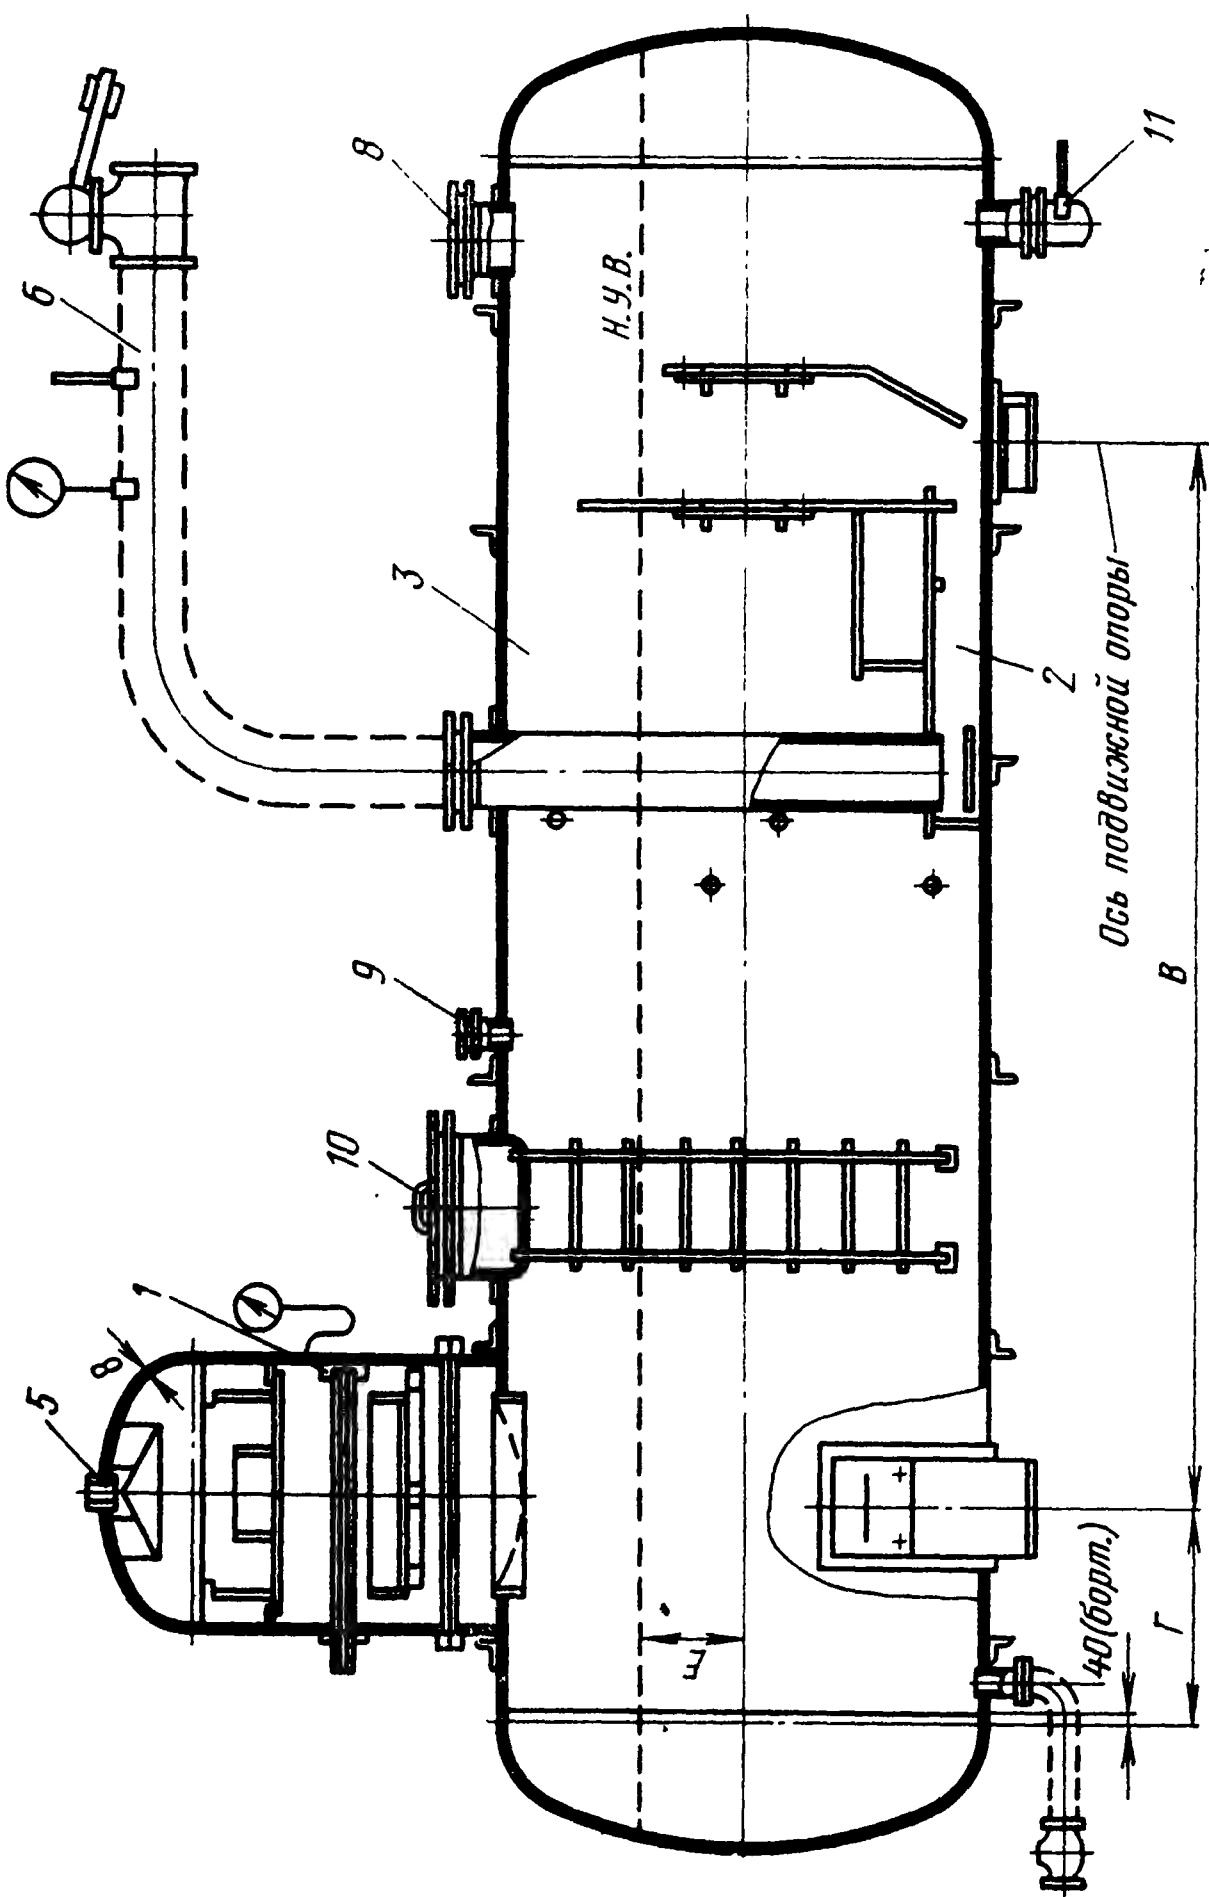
Общий вид двухступенчатого деаэрата атмосферного давления (основные габаритные размеры — см. табл. 13-3).
